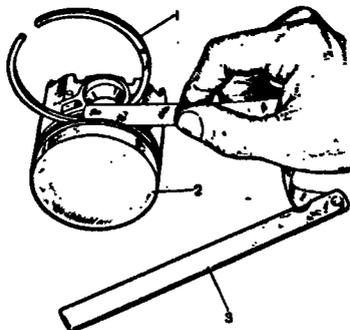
Проверка зазора между поршневыми кольцами и канавками: 1 - поршневое кольцо; 2 - поршень; 3 - набор щупов
